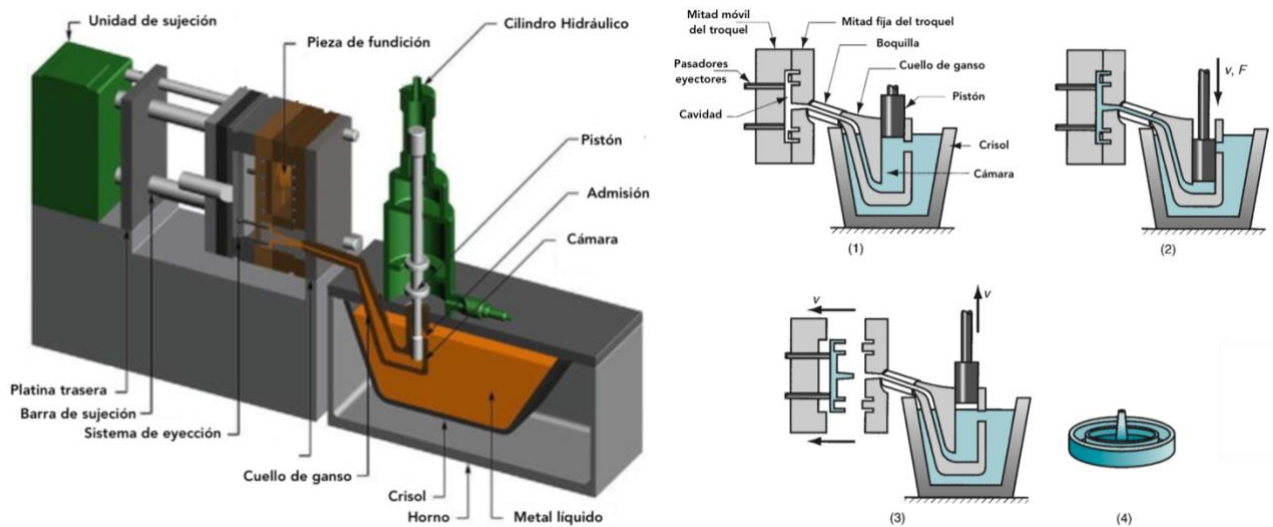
Máquina die casting de cámara caliente (izquierda), adaptado de [3]. Ciclo de la máquina de cámara caliente 1) se cierra el molde y se retrae el embolo, el metal líquido entra en la cámara, 2) el embolo desciende y hace fluir el metal hacia la cavidad del molde manteniendo la presión durante el enfriamiento y solidificación, 3) se retrae el embolo, se abre el molde y la pieza es expulsada, 4) pieza final, adaptado de [2].
